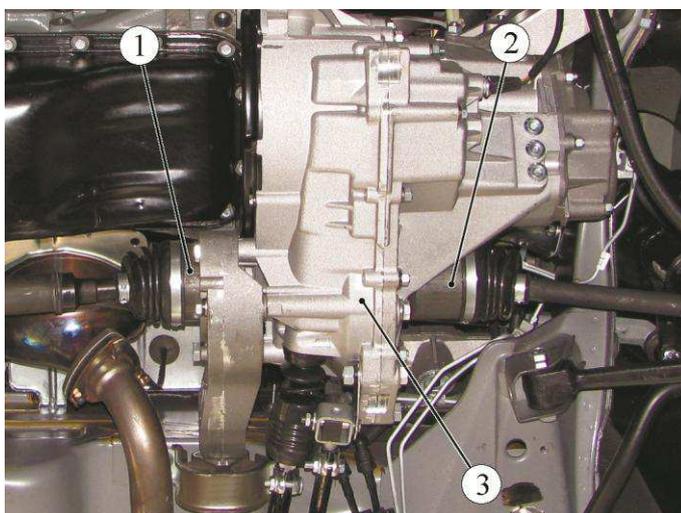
Отсоединение внутренних шарниров приводов от коробки передач:
